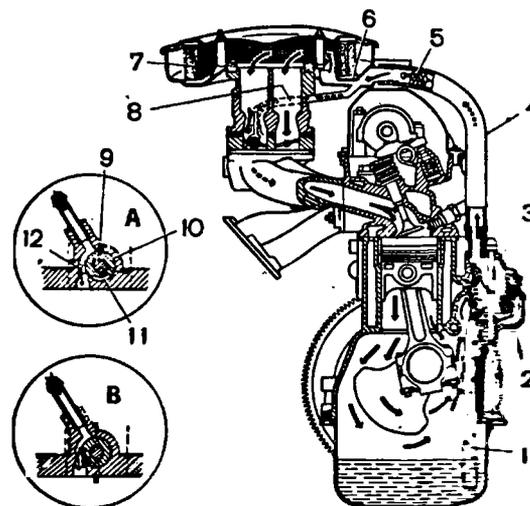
Схема системы вентиляции картера двигателя: А и В - работа золотникового устройства карбюратора при малой частоте вращения коленчатого вала (А) и при высокой (В): 1 - сливная трубка маслоотделителя; 2 - маслоотделитель; 3 - крышка сапуна; 4 - шланг отсоса газов; 5 - пламегаситель; 6 - выхлопной коллектор; 7 - фильтрующий элемент воздушного фильтра; 8 - шланг отвода газов в задрозсельное пространство карбюратора; 9 - ось дроссельной заслонки первичной камеры; 10 - золотник; 11 - канавка золотника; 12 - калиброванное отверстие
